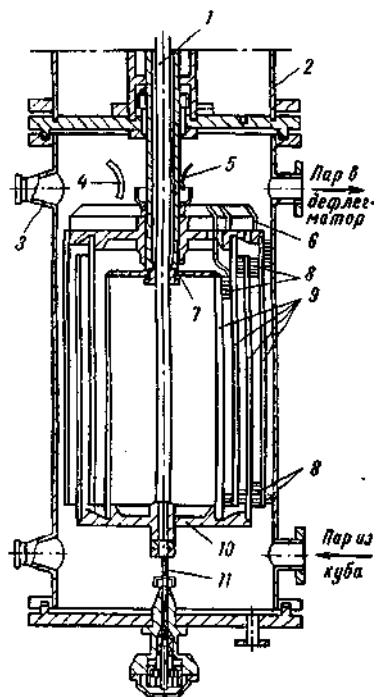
Многоцилиндровая роторная ректификационная колонна: 1 – верхний вал; 2 – цилиндр; 3 – смотровое окно; 4 – труба для подачи флегмы; 5 – подача смазки в подшипник; 6 – распределитель флегмы; 7 – подшипник; 8 – турбулизаторы; 9 – цилиндры ротора; 10 – направляющий фланец; 11 – нижний вал.
